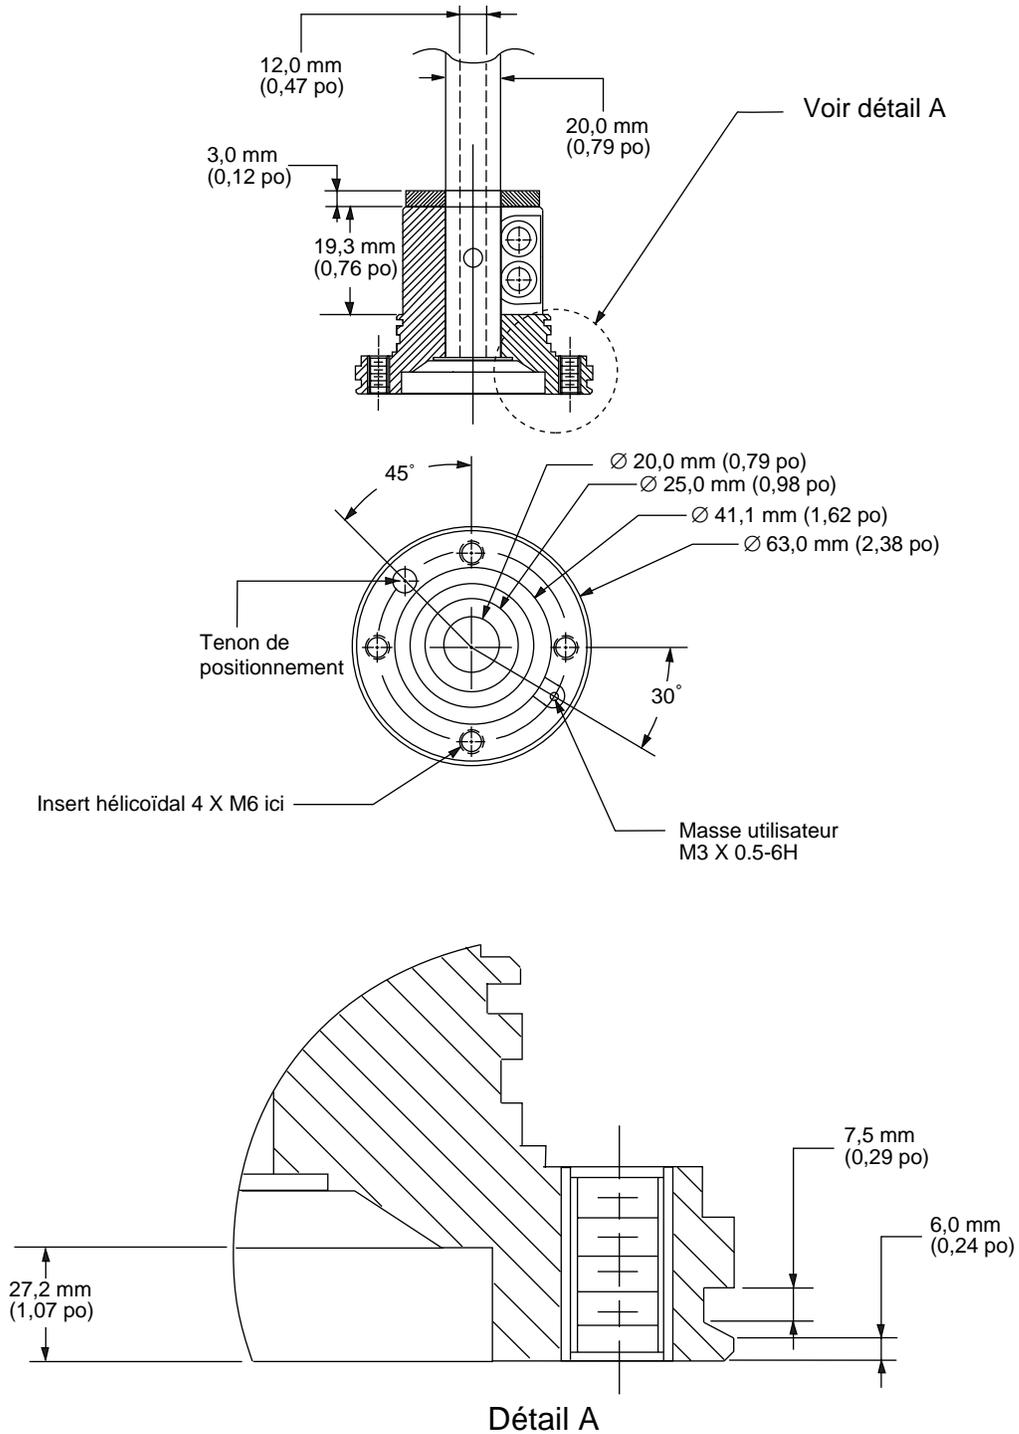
Dimensions de la bride outil du Dimensions latérales et du dessus du robot Adept Cobra 600
